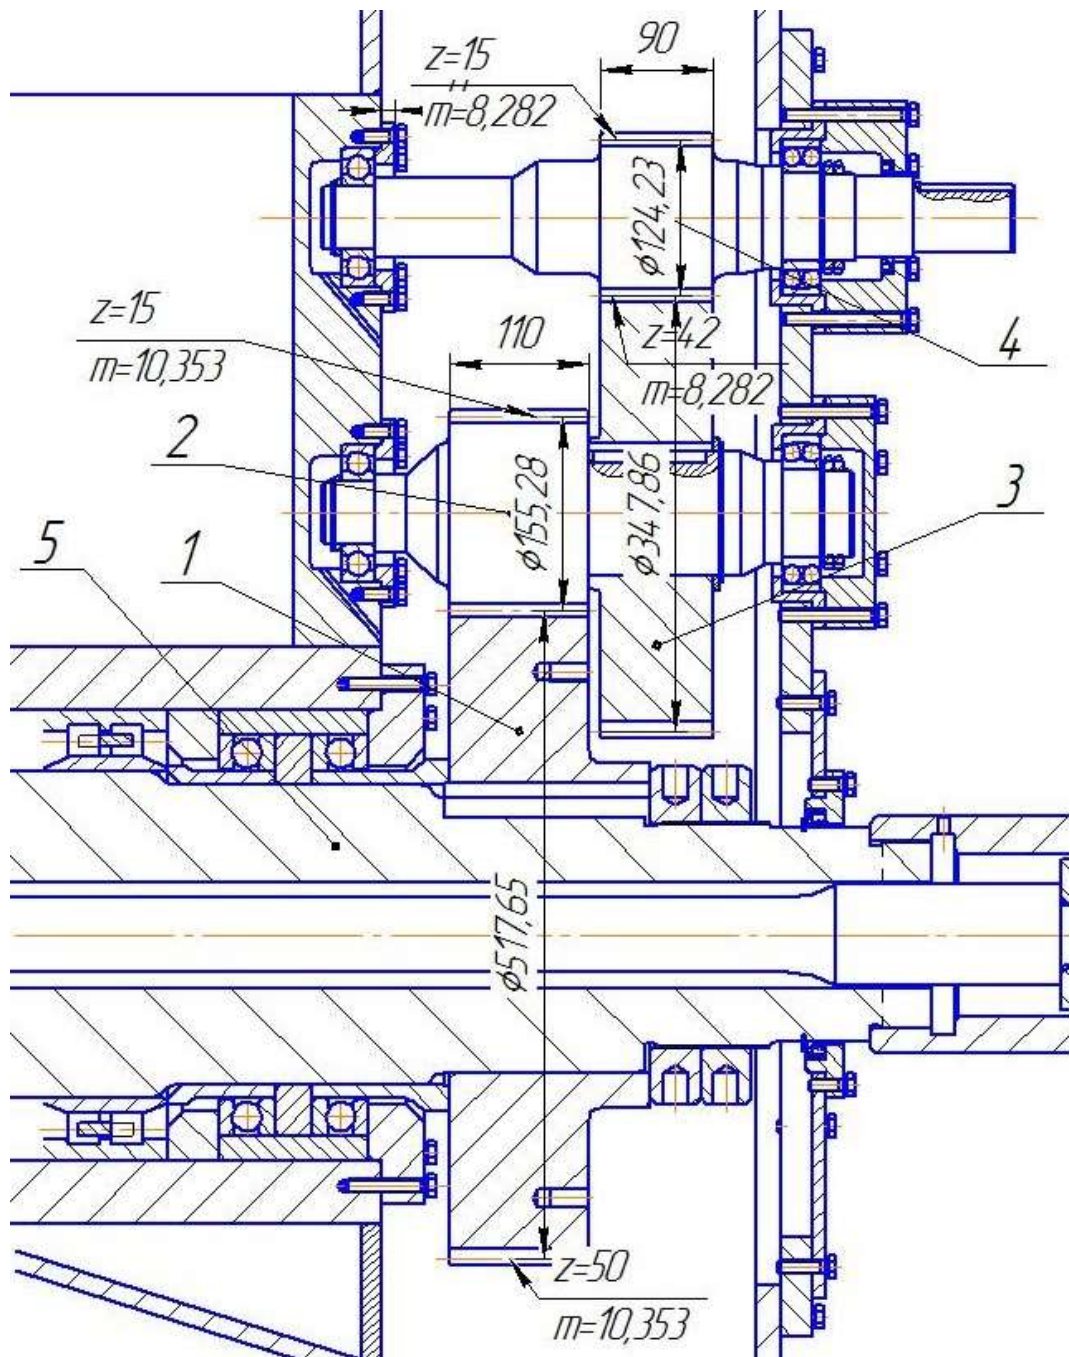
Схема прямозубой цилиндрической передачи
